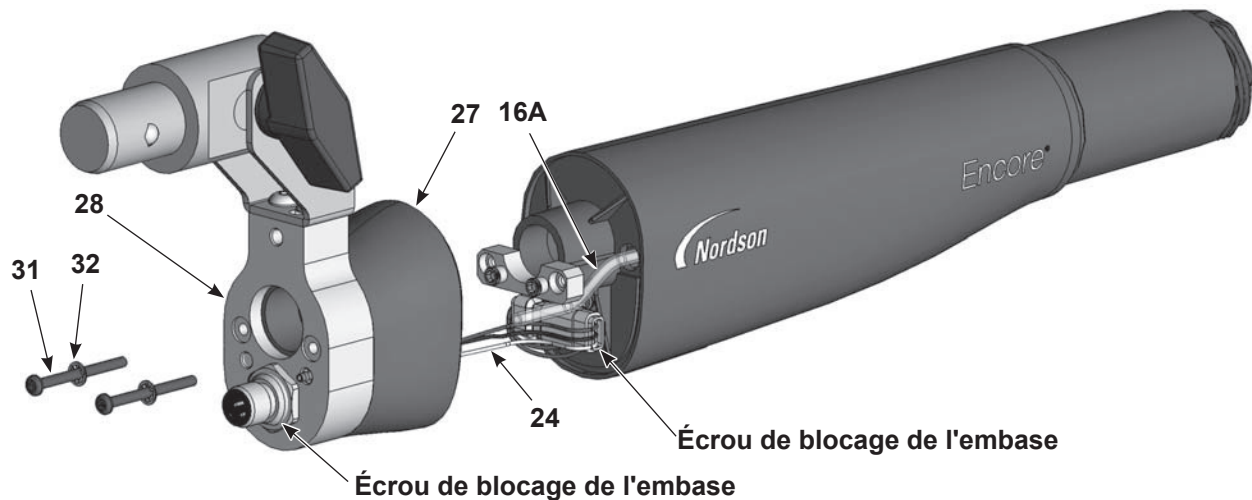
Démontage du pistolet – Remplacement du tube à poudre
